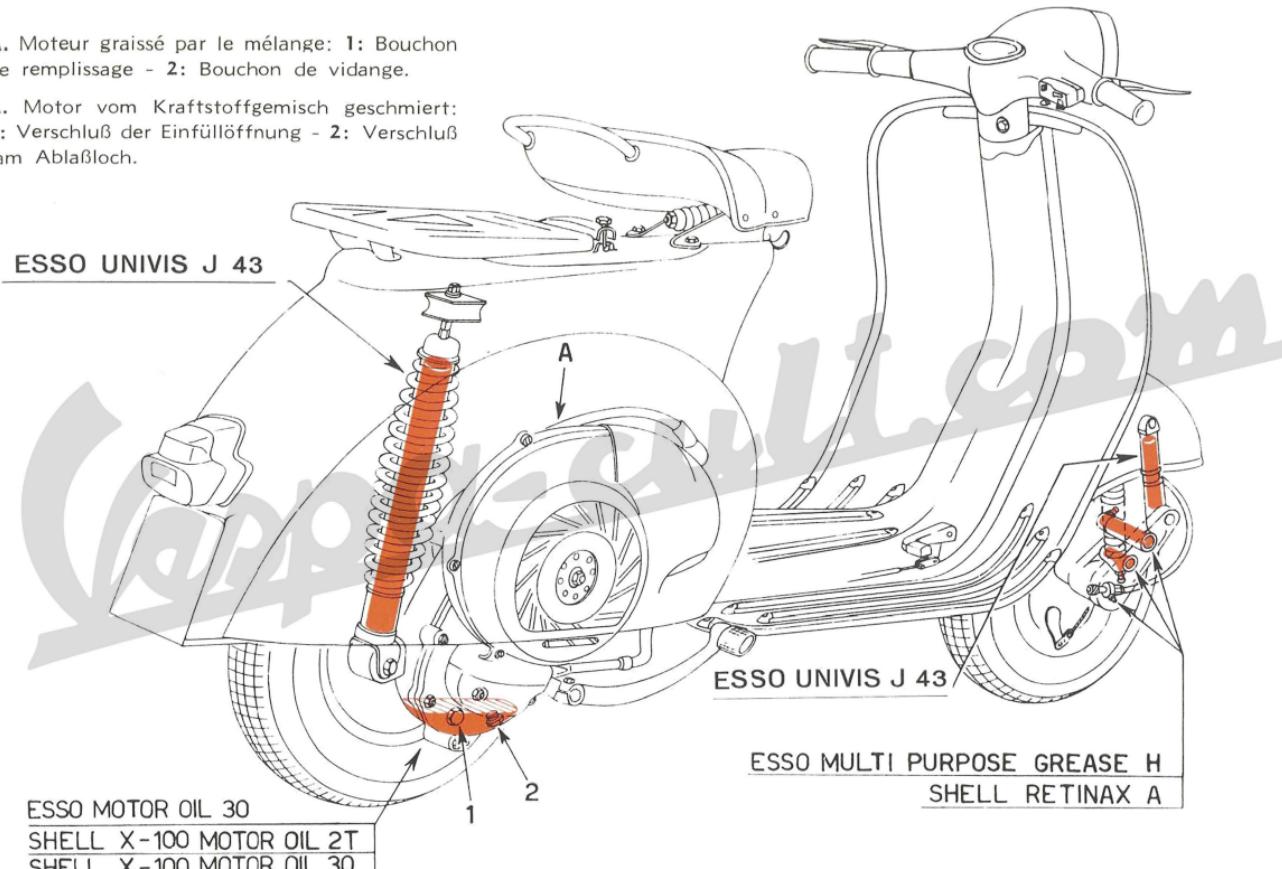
Graissage du scooter - Abb. 23 - Schmierung des Fahrzeuges
